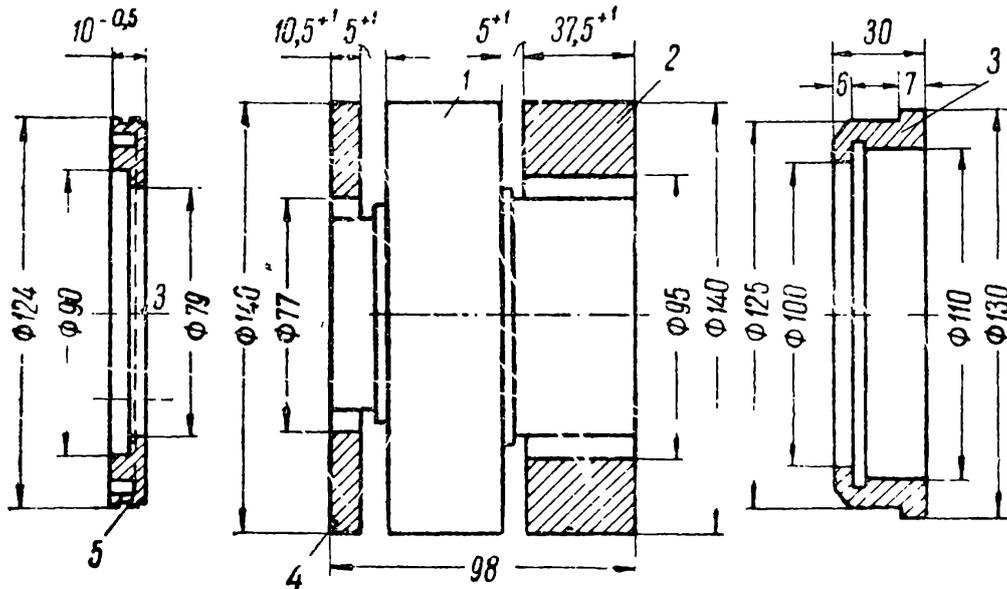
Совместное изготовление заготовок трех различных деталей из одной болванки:
